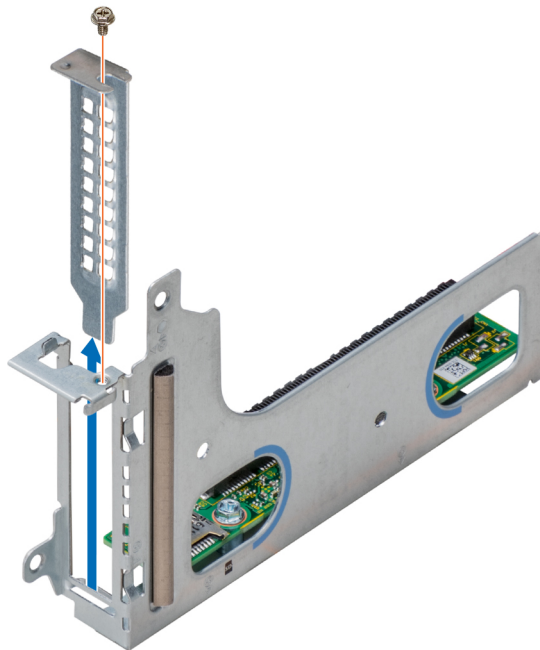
Retrait du support de la plaque de recouvrement de carte d'extension
